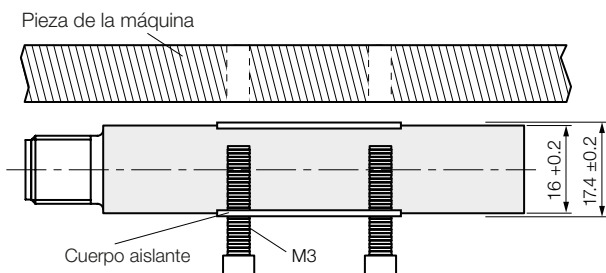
Montaje de la cabeza de sensor con cuerpo aislante
